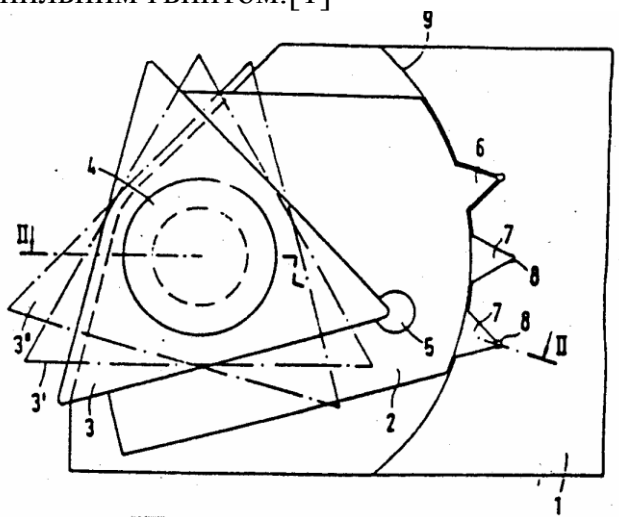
Конструкція різця, що забезпечує дискретне регулювання поворотної підкладки з БНП: 1 - державка; 2 - поворотна підкладка; 3 – різальна пластина; 4 – гвинт.[12]
